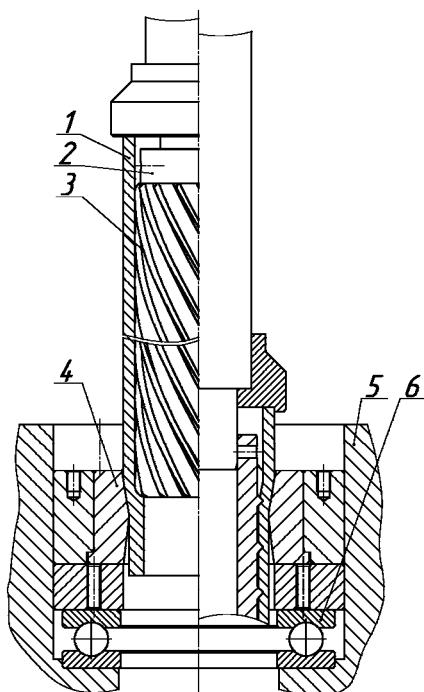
Общий вид схемы редуцирования: 1 – трубная заготовка; 2 – пuhanсон; 3 – многозаходные спиральные выступы; 4 – матрица; 5 – корпус штамповой оснастки; 6 – шариковый радиально-упорный подшипник
